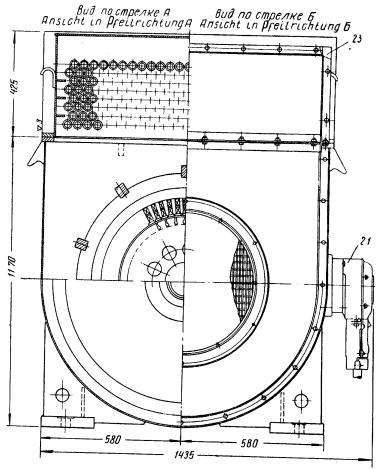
Общий вид асинхронного двигателя ДАЗО-14: I- шпонка ШОК32 \times 18 \times 200 НКМ4085; 2- щит подшипинковый; 3- щит; 4- ротор; 5- статор; 6- болт М16 \times 40; 7- болт М12 \times 30; 8- воздухоохладитель; 9- болт М10 \times 18; 10- кожух; 11- гайка М10 ГОСТ 5927-51; 12-6олт М10 \times 22; 13- кожух; 14- щит; 15-6олт М16 \times 70; 16- диффузор; 17- вентилятор;
